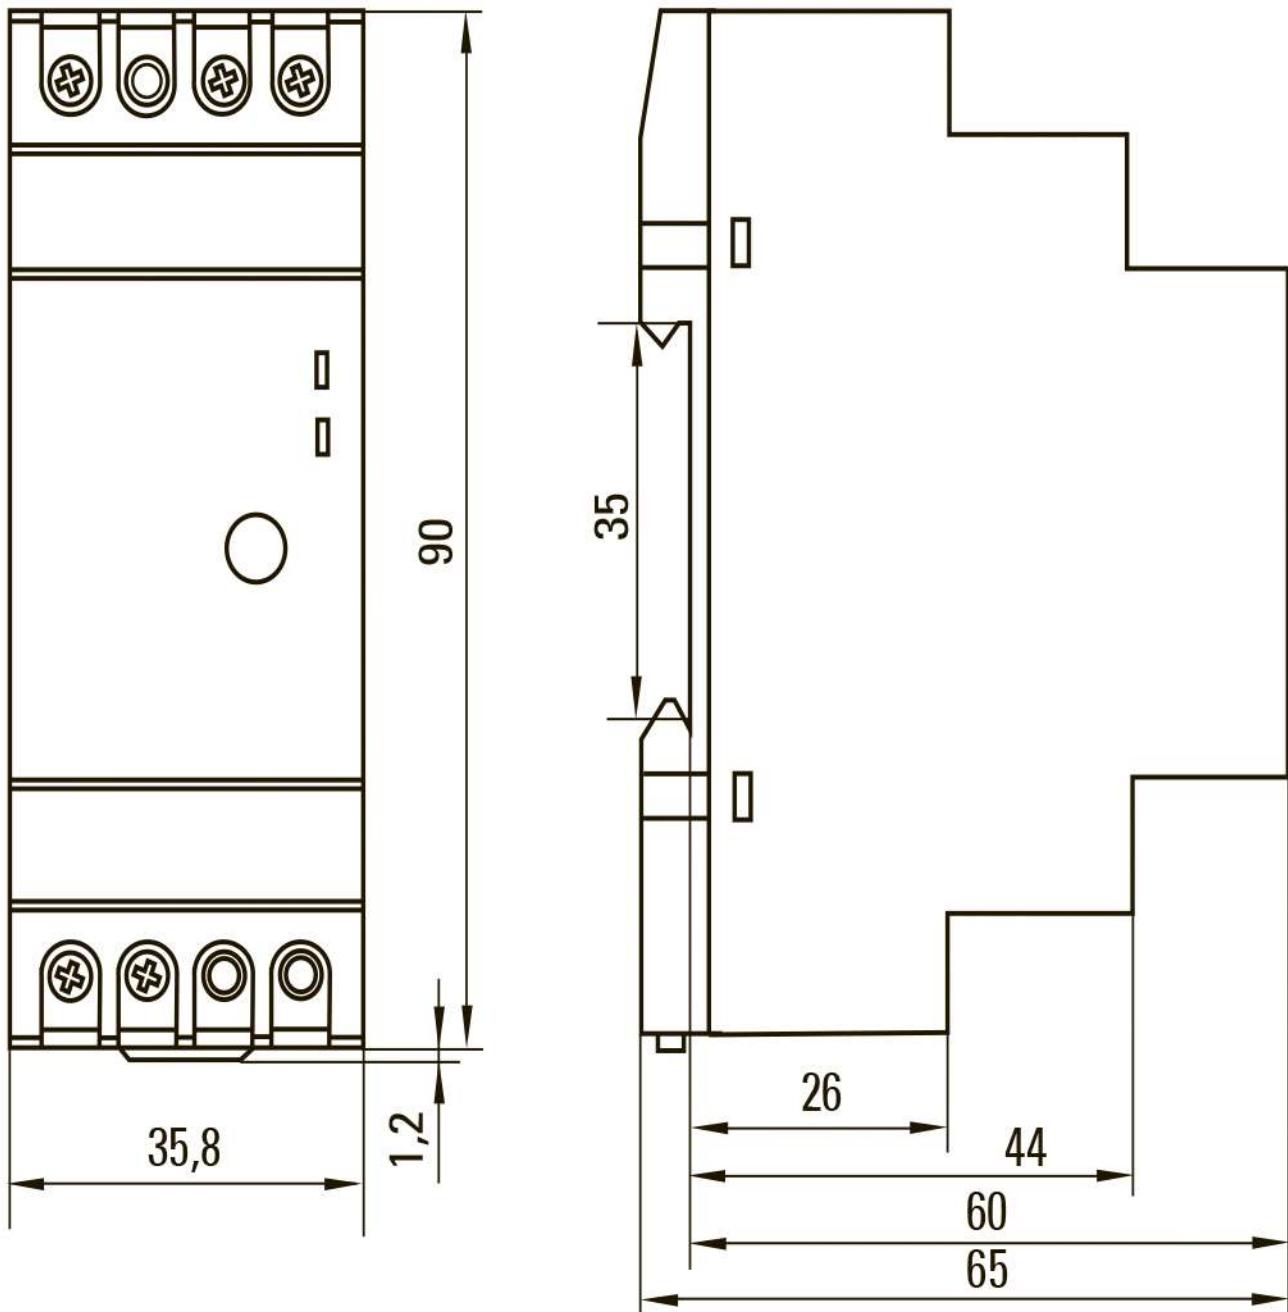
Габаритные размеры фотореле DIN-1 (ФР)
